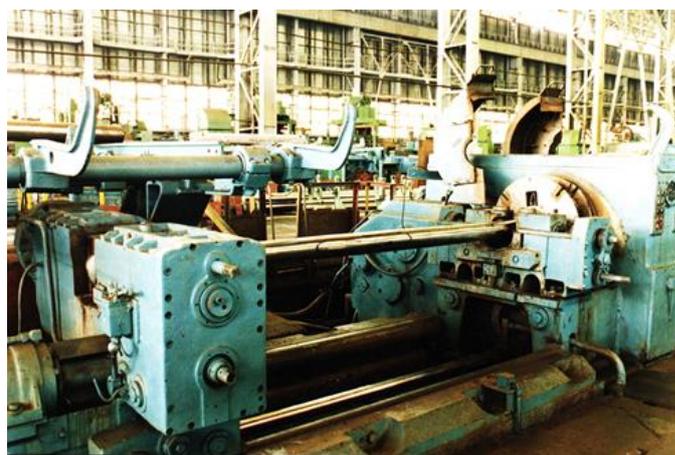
Бесцентрово-токарный станок с роликковой клетью
